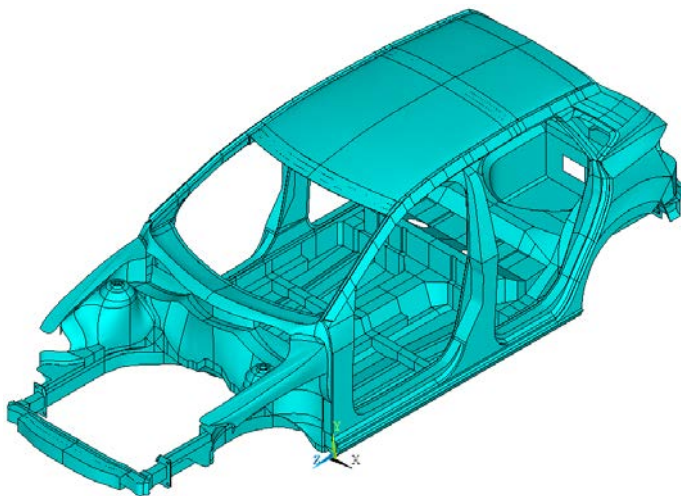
Схема кузова легкового автомобиля, изготовленного из одной марки стали
